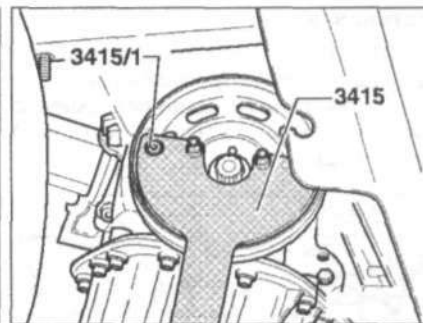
в. Снимите шкив и открутите центральный болт крепления шкива ремня ГРМ, удерживая шкив с помощью приспособлений 3415 и 3415/1.
